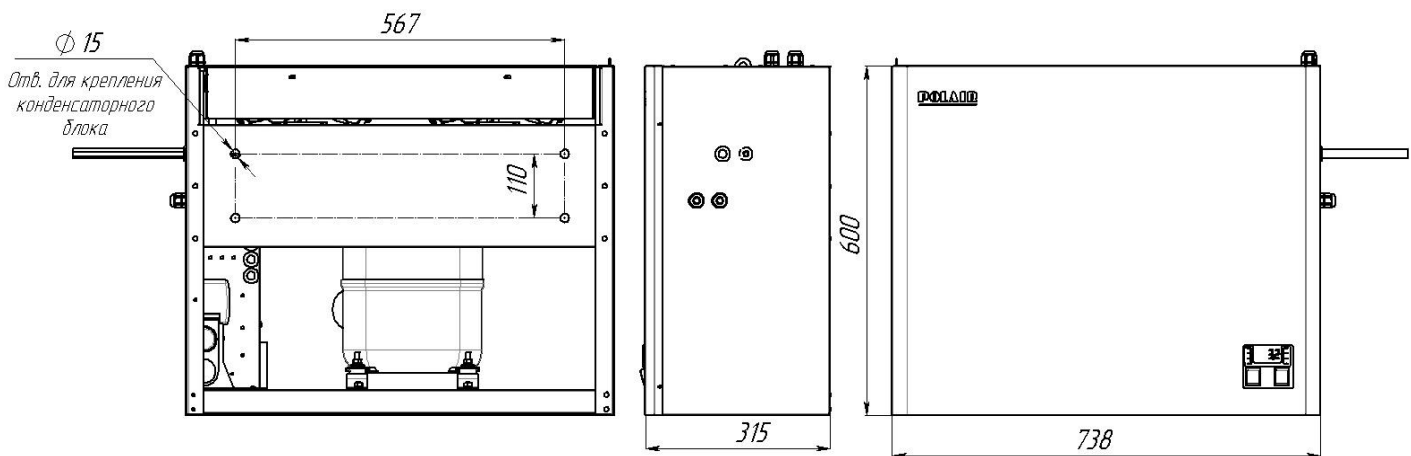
Габаритные и присоединительные размеры конденсаторного блока сплит-систем второго габарита
